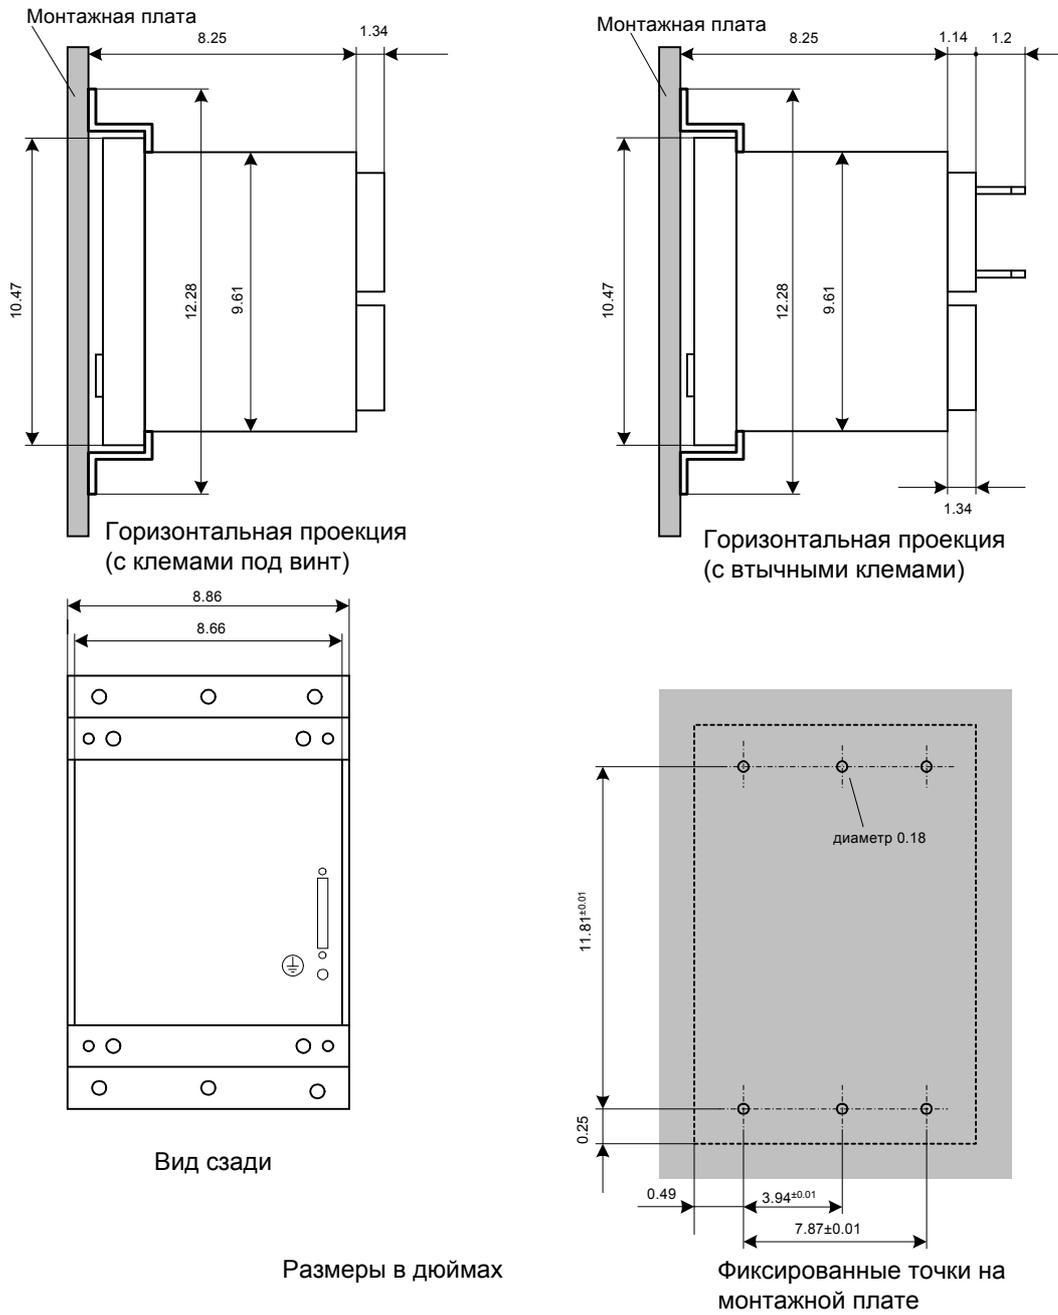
Размеры устройства 7SJ63 с отдельной панелью управления (размер корпуса 1/2)
